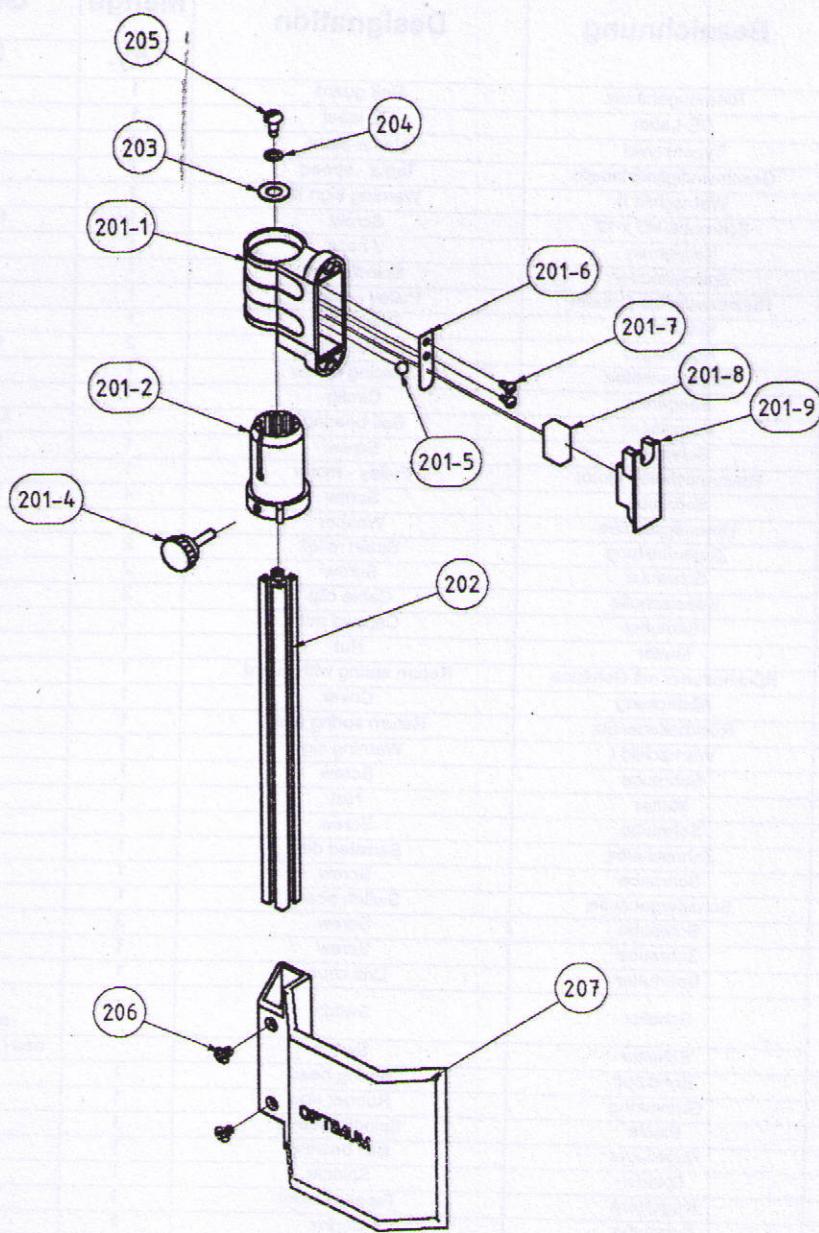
Bohrfutterschutz B17 Pro - Drill chuck protection B17 Pro
